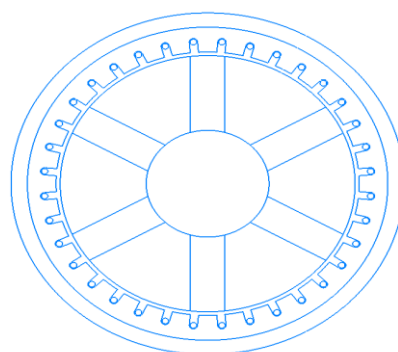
Примерный общий вид синхронного двигателя с ферритовыми магнитами
